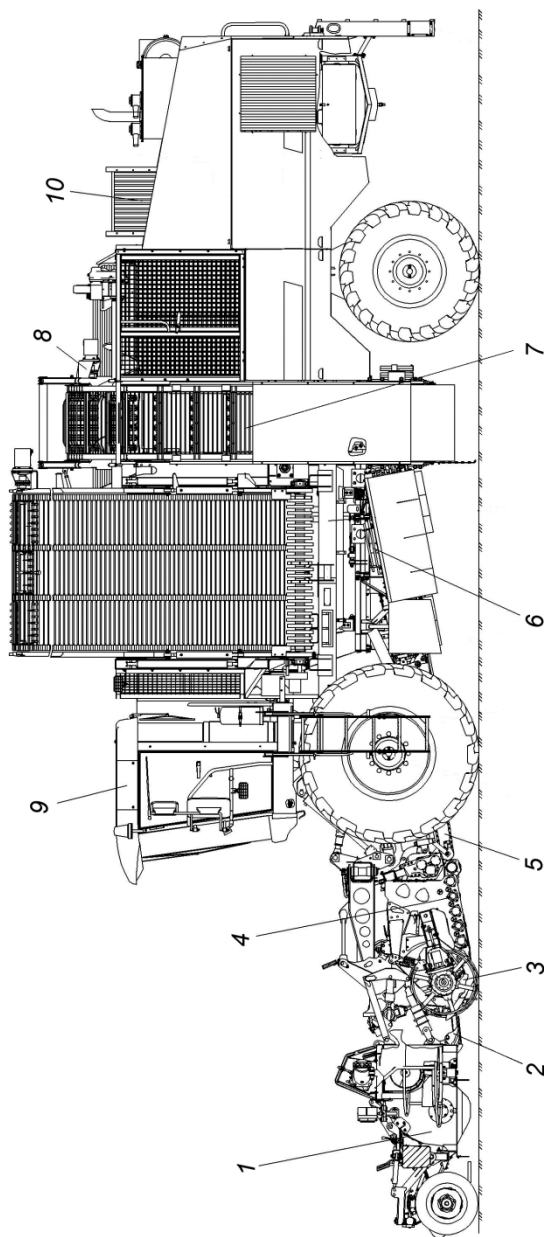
Самоходный свеклоуборочный комбайн: 1 – ботворез; 2 – дообрезчики; 3 – копачи; 4 – шнековый очиститель; 5 – прутковый транспортер; 6 – дисковый очиститель; 7 – загрузочный транспортер; 8 – бункер; 9 – кабина; 10 – двигатель
